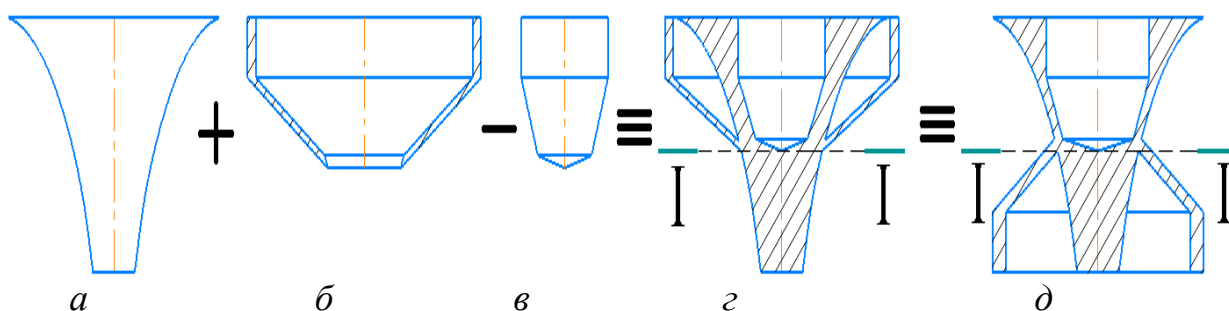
Способ встраивания бойка с криволинейной образующей боковой поверхности, где:
